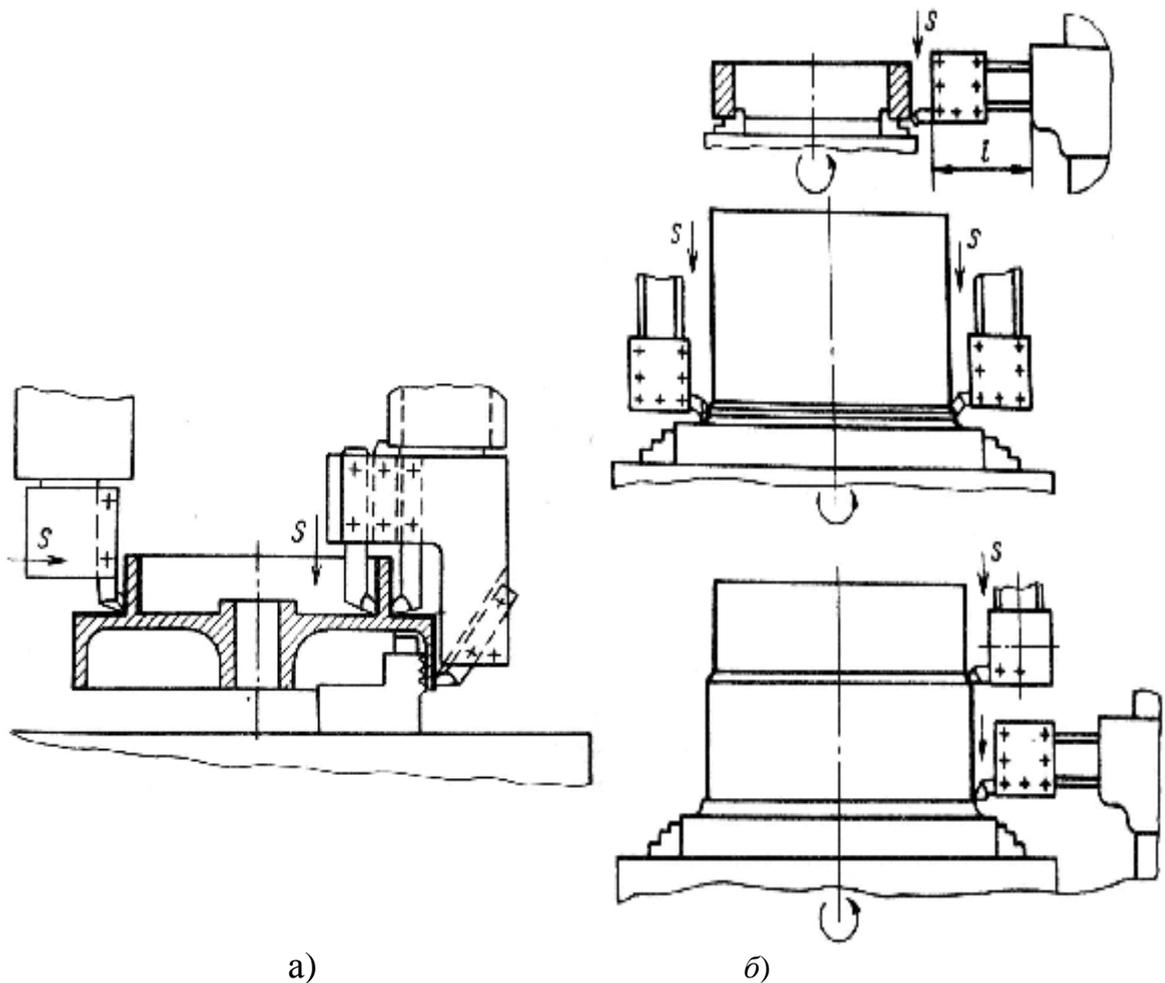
Схемы многоинструментальной обработки крупногабаритной заготовки (а) и обтачивания цилиндрических поверхностей (б)
